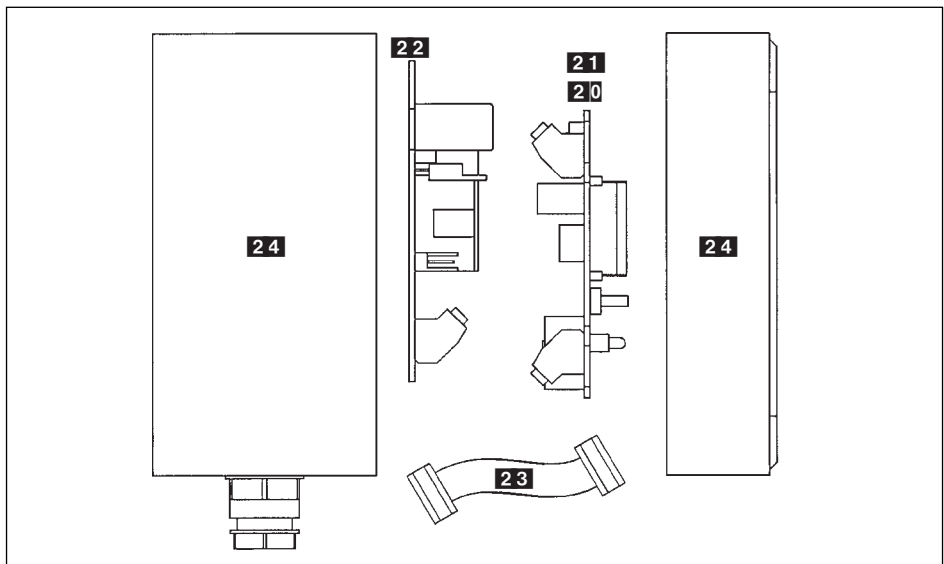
Ersatzteil-Explosionszeichnung Wandmontage-Ausführung
